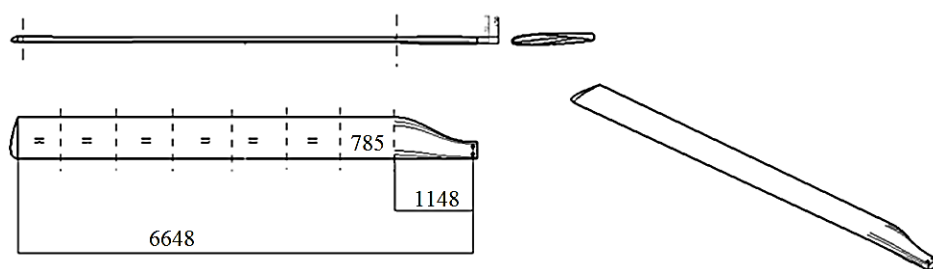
Géométrie et dimensions de la pale d'hélicoptère.
